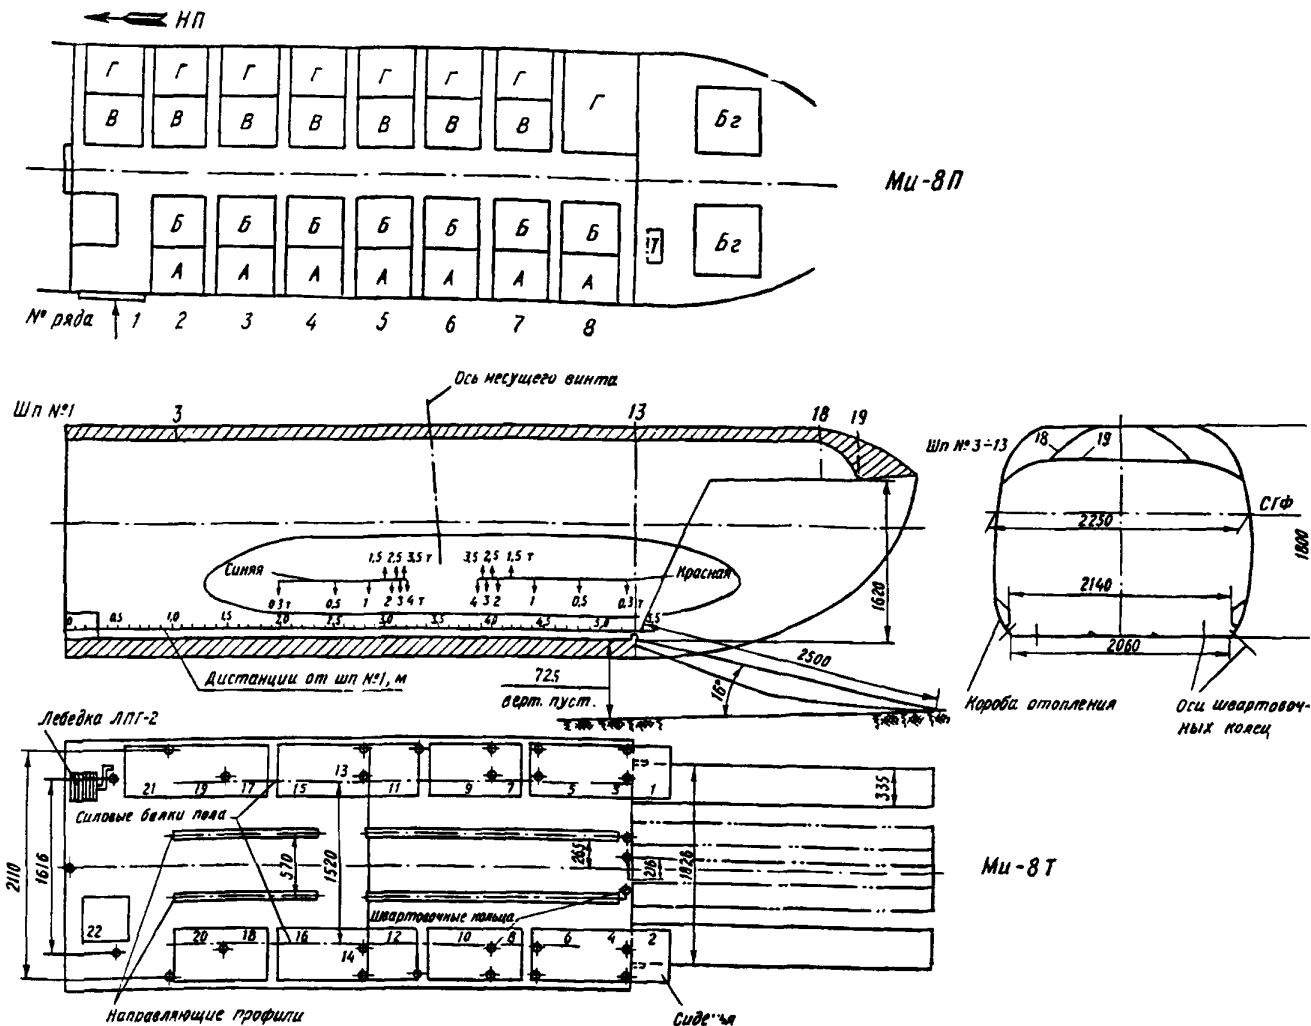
Компоновка пассажирской и грузовой кабины вертолета Ми-8
